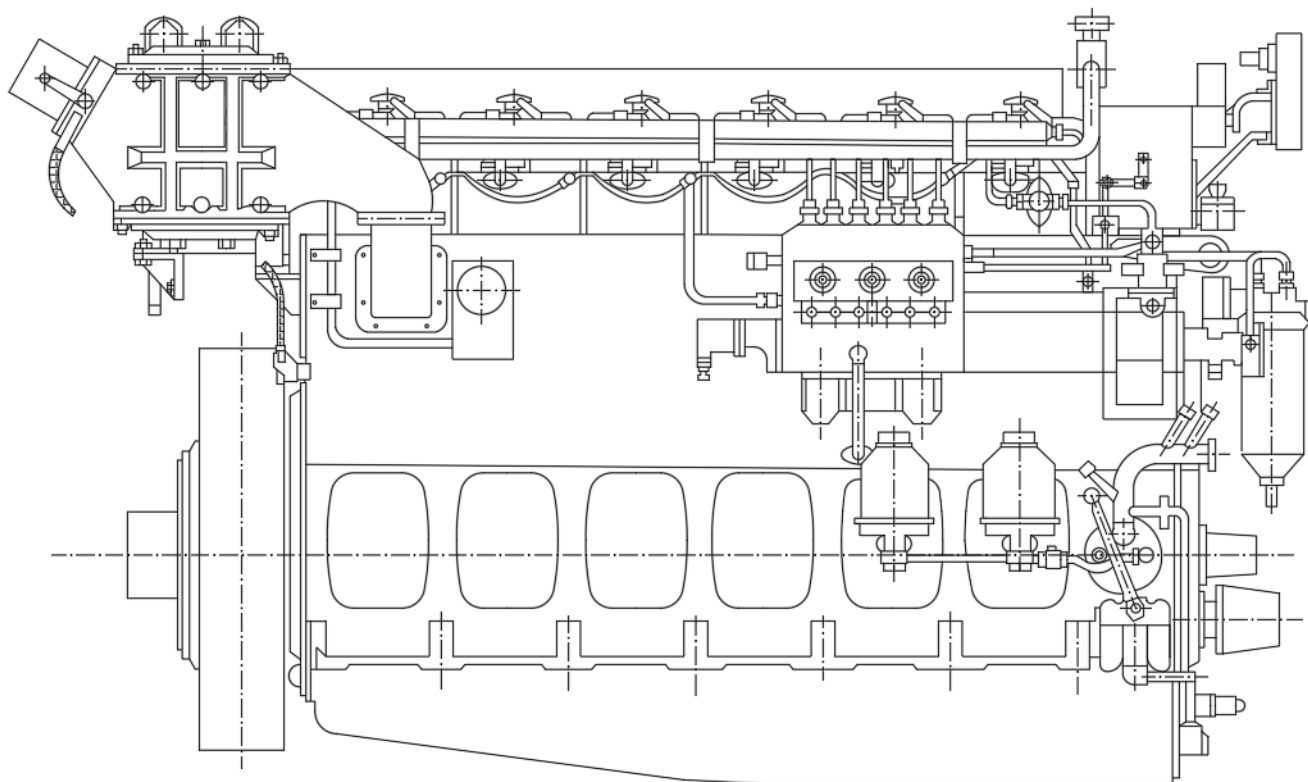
Продольне креслення двигуна 6ЧН 18/22
